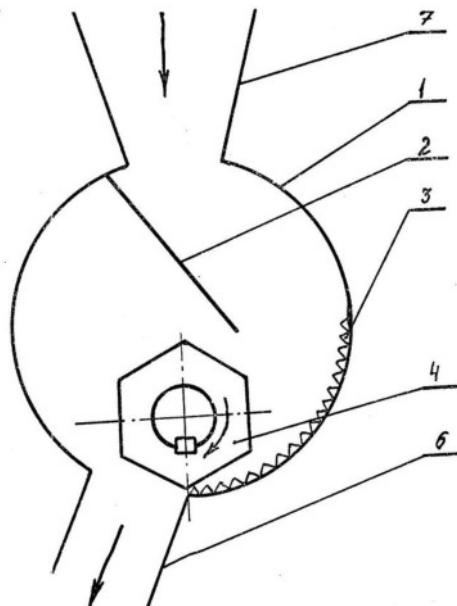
Общий вид прощенной конструкции дробилки кормов по патенту РФ № 2105609
